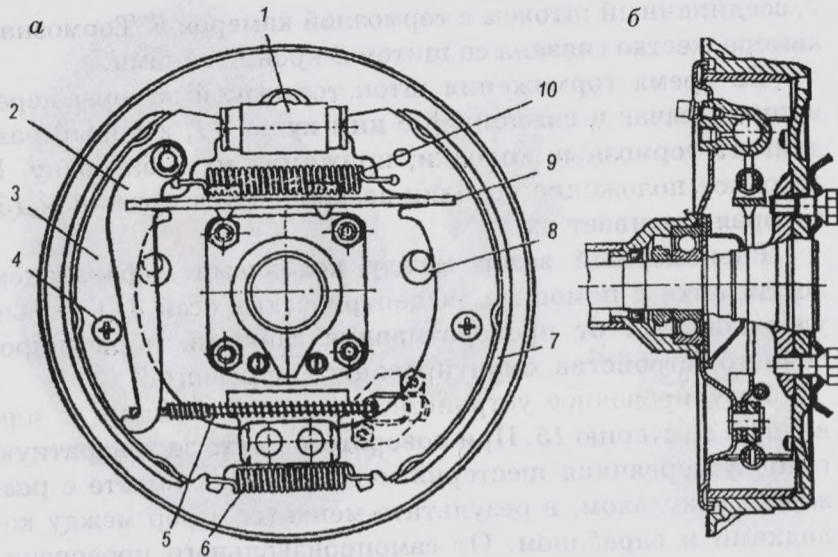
Тормоз заднего колеса автомобиля ВАЗ-2101: а – общий вид (тормозной барабан снят); б – поперечный разрез; 1 – колесный цилиндр; 2 – рычаг ручного привода; 3 – колодка тормоза; 4 – чашка и опорная стойка колодки; 5 – трос привода ручного тормоза с оболочкой; 6 – нижняя стяжная пружина; 7 – фрикционная накладка; 8 – эксцентрик регулировки зазора между колодкой и барабаном; 9 – распорная планка; 10 – верхняя стяжная пружина
